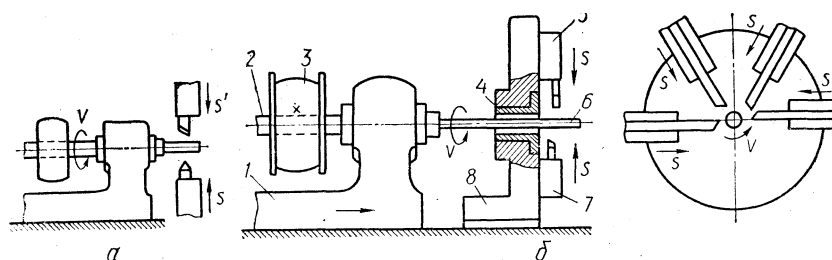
Схеми обробки на одношпиндельних токарних автоматах
